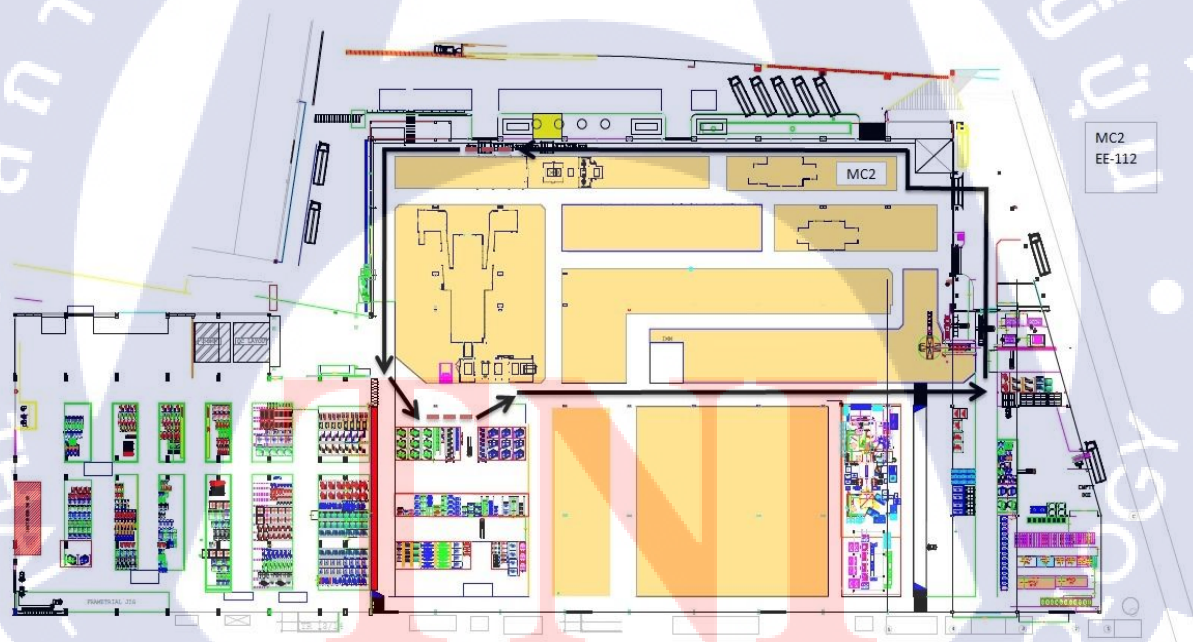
LAYOUT เส้นทางขนส่งของรถสามล้อ MZ-01
